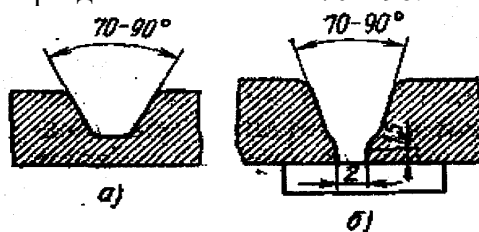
Профили разделки дефекта под пайку - сварку: а - разделка несквозного дефекта, б - разделка дефекта с применением подкладки из огнеупорного материала
